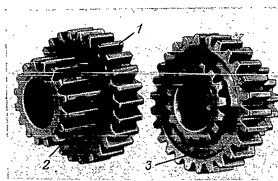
Ведущее зубчатое колесо редуктора (собранное).
